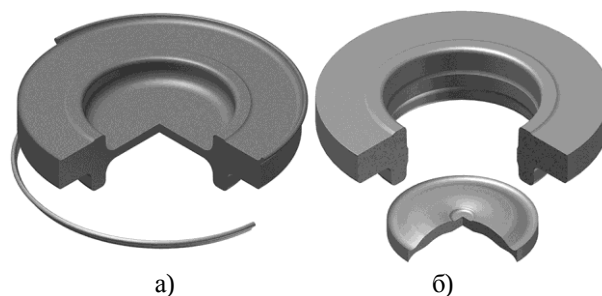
Типовая технология изготовления поковки каретки синхронизатора: а) – предварительная штамповка, б) – окончательная штамповка
